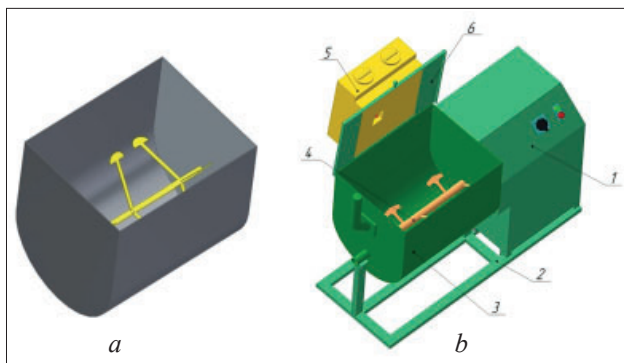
СВЧ-установка для термообработки субпродуктов высокой влажности: *a* – общий вид установки; *b* – объемный резонатор с лопастной мешалкой; 1 – шкаф управления; 2 – станина; 3 – резонаторная камера; 4 – лопастная мешалка; 5 – СВЧ-генератор; 6 – крышка
